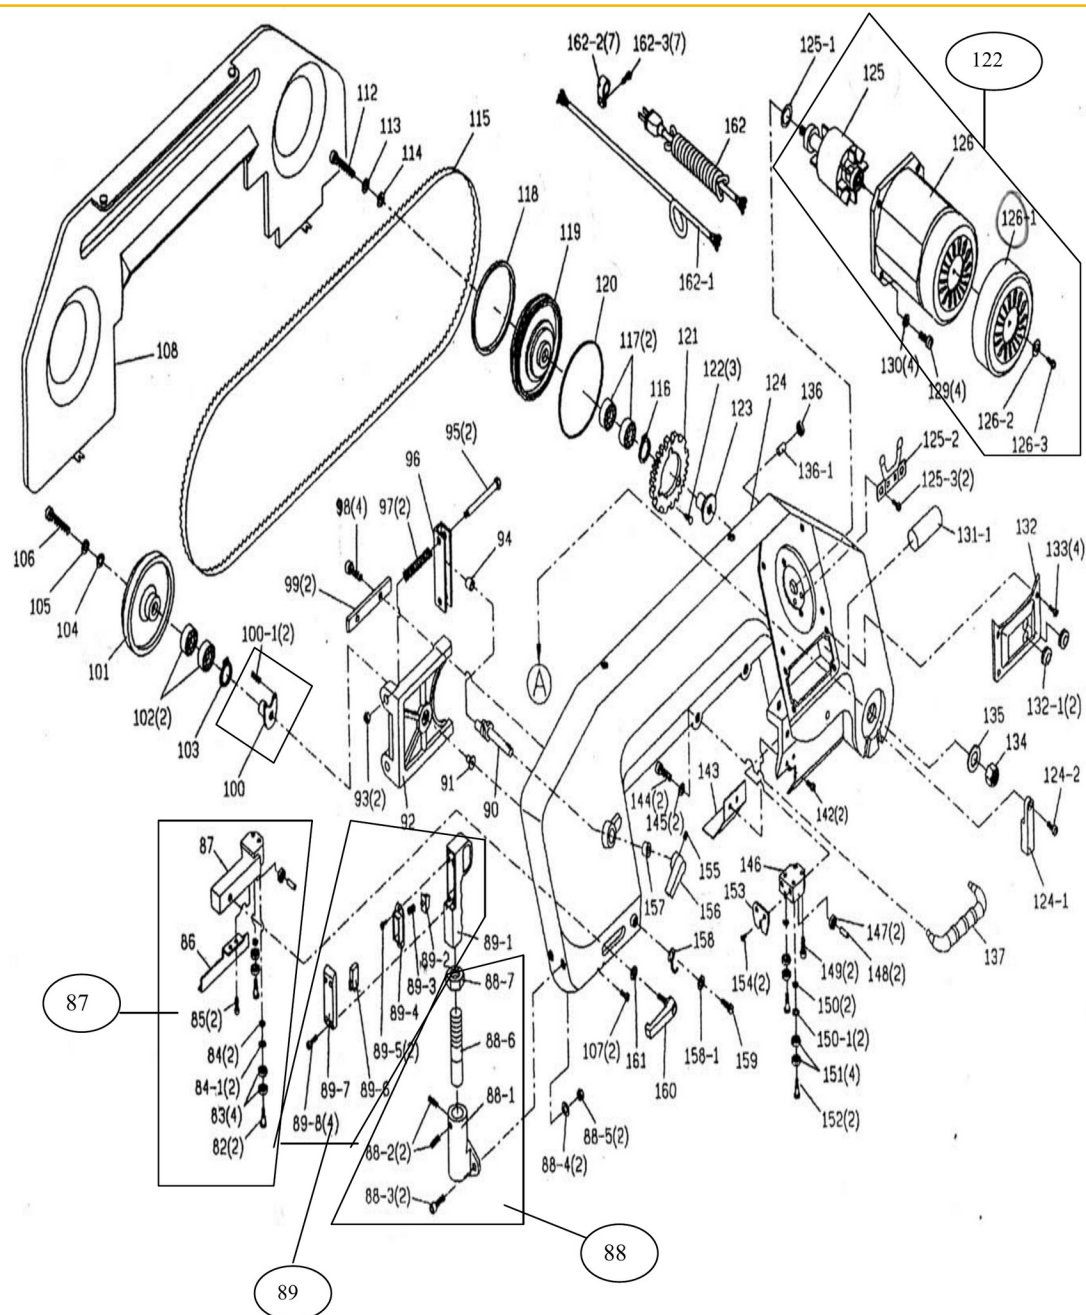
Despiece — brazo de la sierra, transmisión y motor
